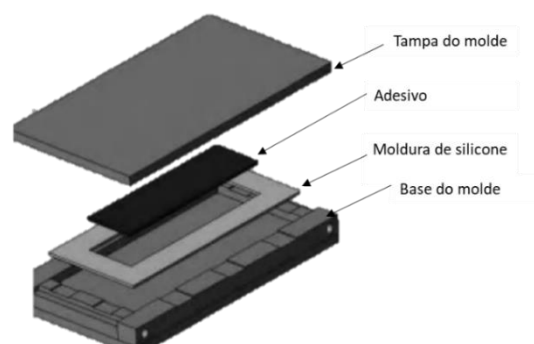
Vista explodida do molde de acordo com a norma NF T 76-142 [18].
